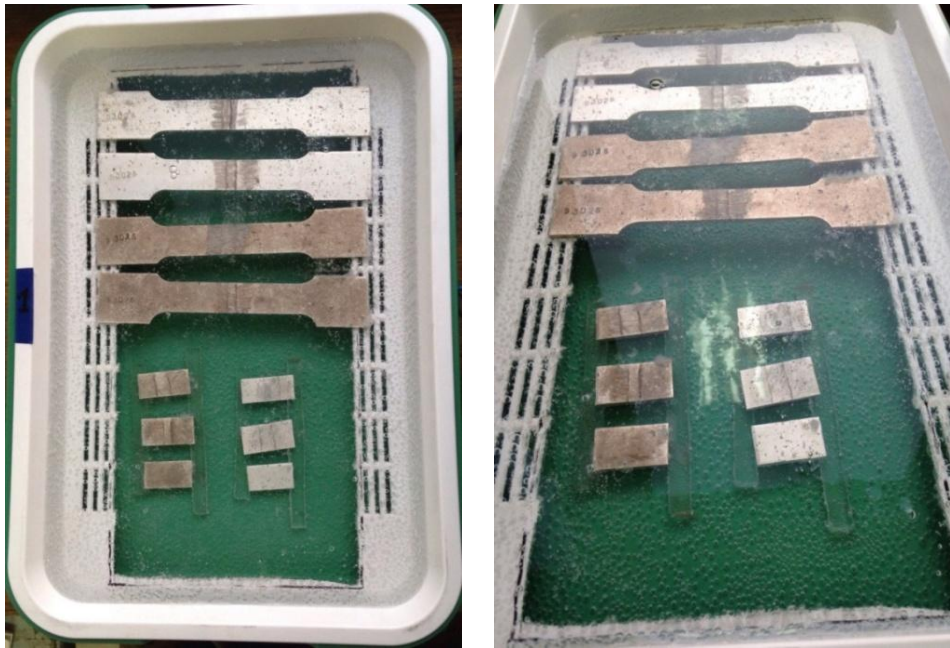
Схема расположения образцов для испытаний на МКК
